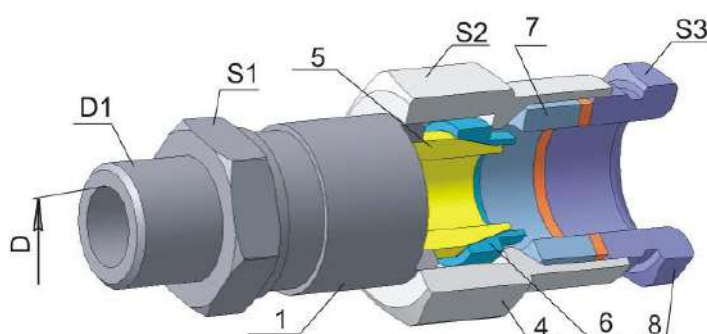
Конструкция кабельного ввода для монтажа бронированного кабеля
